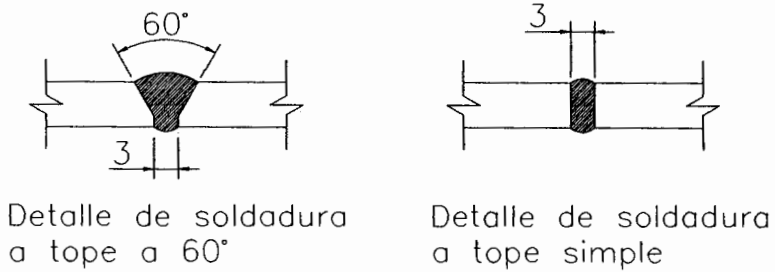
TIPOS DE SOLDADURA
